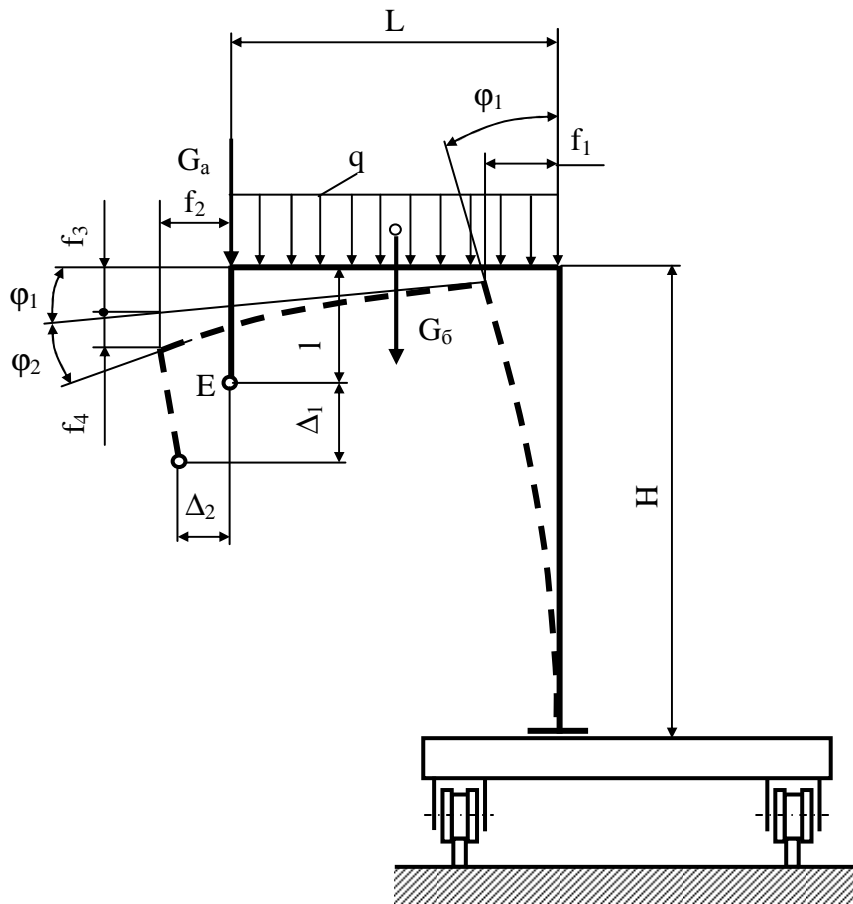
Розрахункова схема несучої конструкції зварювального візка
